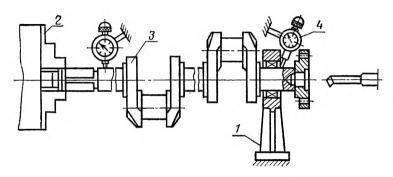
Схема установки коленчатого вала на токарном станке для обработки гнезда под подшипник:
